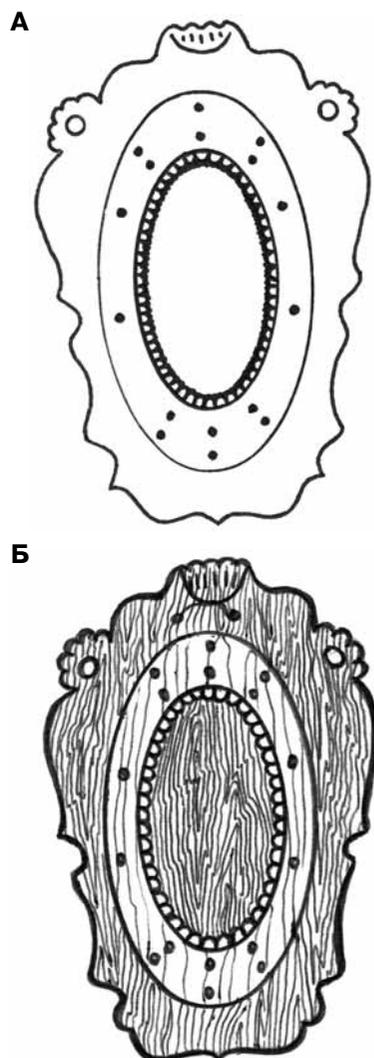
Овальная цельнорезная рама: А — заготовка; Б — заготовка с привинченной фанерной подложкой.
